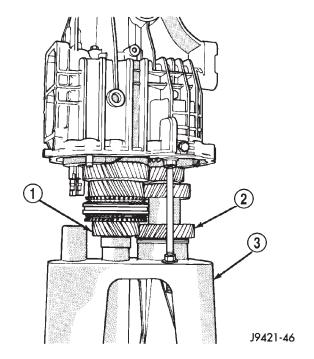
HORMA DEL TREN DE ENGRANAJES Y CUBIERTA
